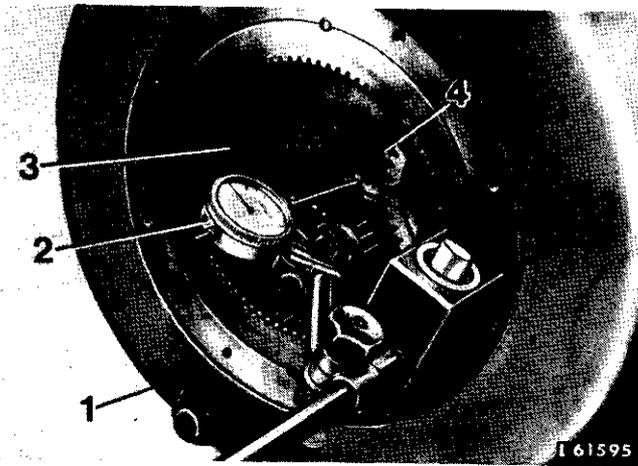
Contrôle du jeu axial de l'arbre d'un moteur hydraulique
